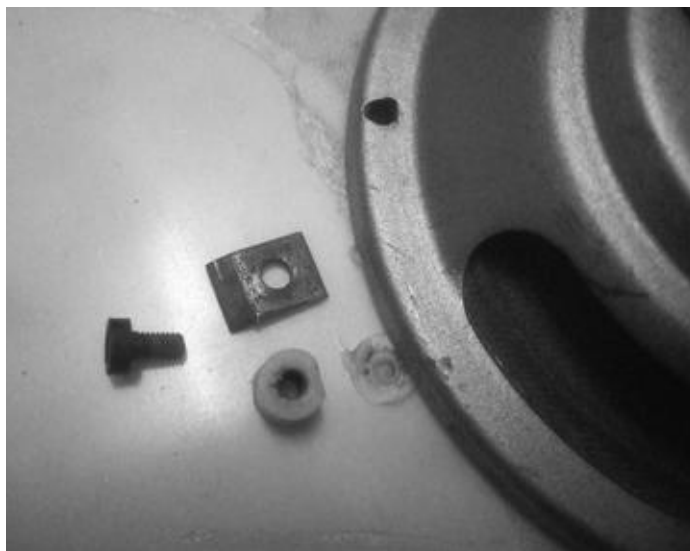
Schwachpunkt: Die in Kunststoff eingepressten Gewindebushen für die Lautsprecherbefestigung brechen leicht ab. Wenn diese noch vorhanden sind, lassen sie sich mit Kunststoffkleber wieder befestigen.
